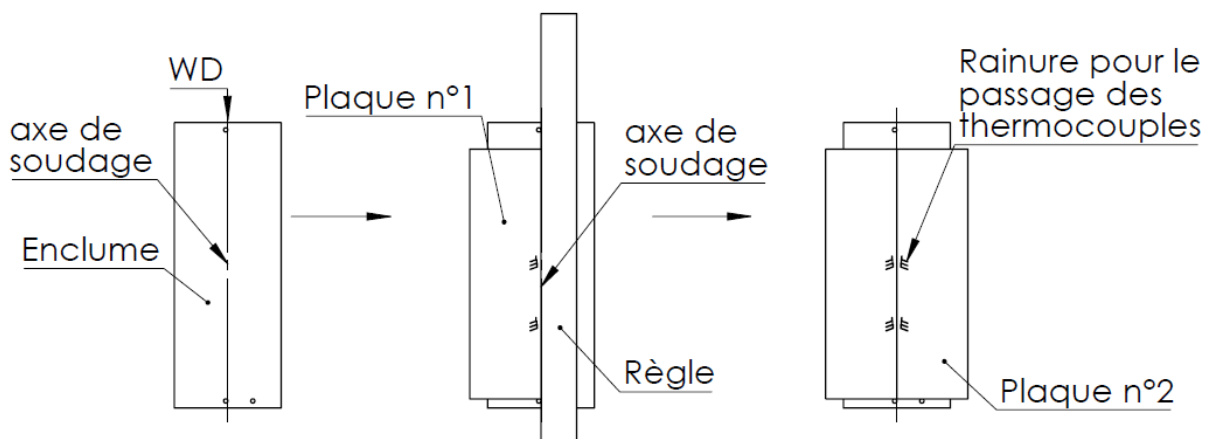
Système permettant un placement précis des plaques avant bridage
